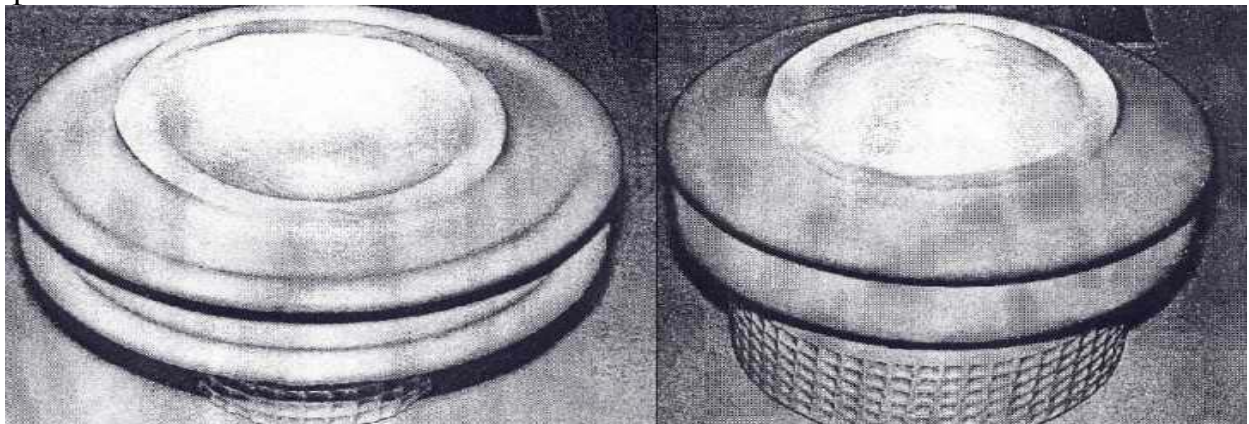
Обмежено-об'ємний дефект. Виникає під час порушення режиму витяжки заготовки ізолятора з вакуум-преса. ОСІ ОНС-20-500. ЛФЗ. Виявлений УЗНК
